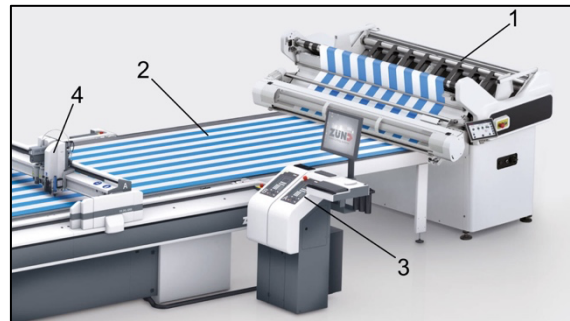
Aufbau CNC-Schneidmaschine [79]
